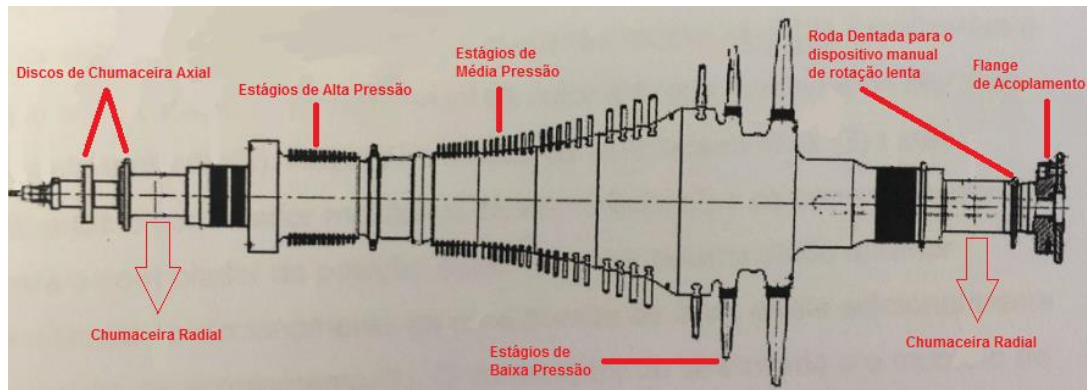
Vista em corte axial do rotor da turbina SST-800 [46]
